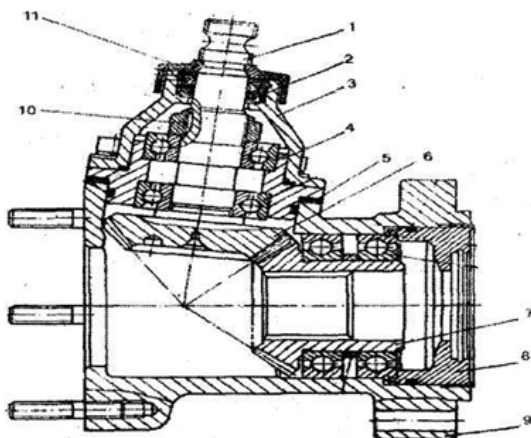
Угловой редуктор: 1 - ведущий вал с шестерней; 2-уплотненис; 3- крышка корпуса; 4 -корпус подшипников; 3 - регулировочные прокладки; 6,7 - ведущая и ведомая шестерни; 8 - упорная крышка; 9 - корпус редуктора; 10-гайка; 11 - защитная крышка.
